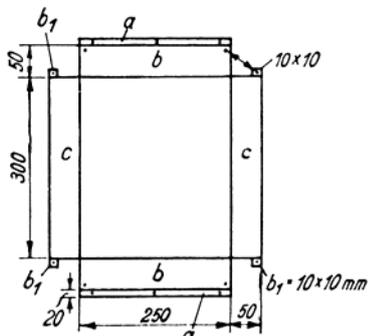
Maßzeichnung für den Blechzusschnitt zum Aufbaugestell.
